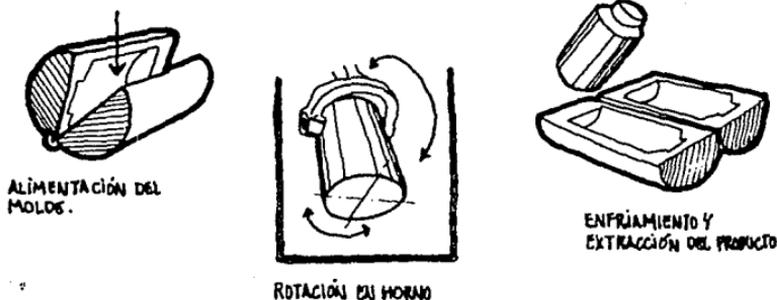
Elementos básicos del Proceso de Rotomoldeo o Moldeo rotacional
